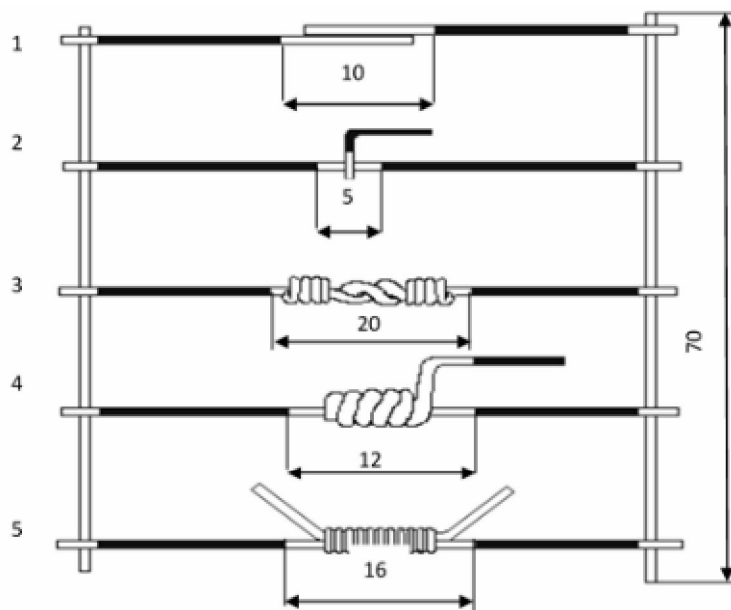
Типы монтажных соединений жил проводов: 1 – соединение внахлест двух проводников; 2 – колечком (отвод от основного провода); 3 – скрутки двух проводов; 4 – навивкой (отвод от основного провода); 5 – бандажированием
